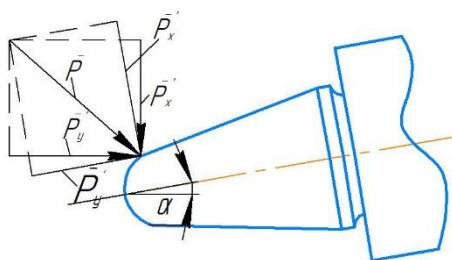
Розкладання повного зусилля, що діє на валок вздовж осі обертання валка та вздовж осі обертання заготовки
